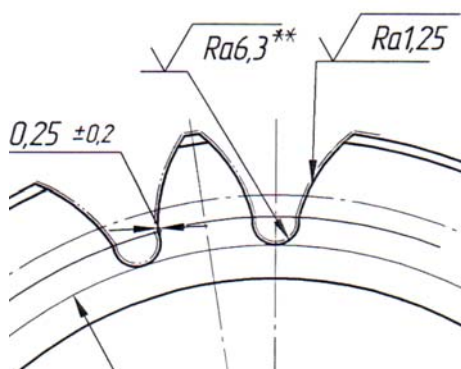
Профиль впадины зуба крупномодульных зубчатых колес
